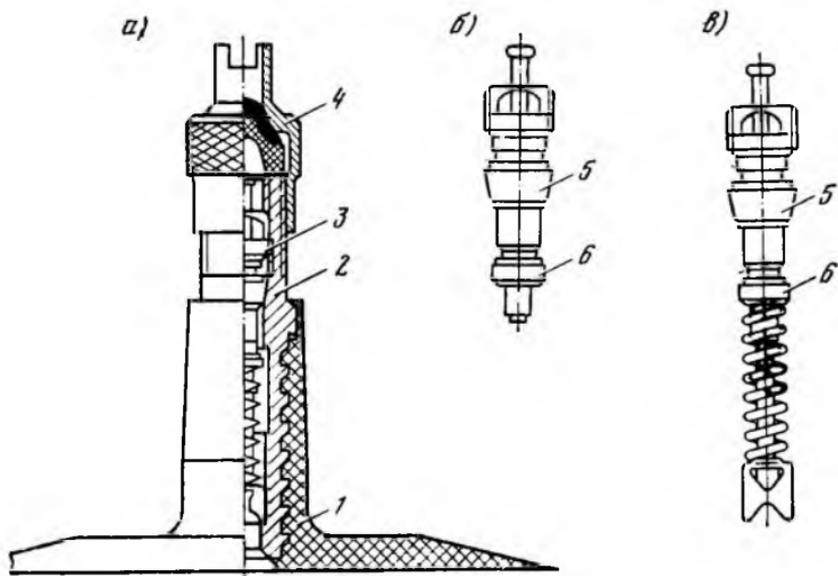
Вентиль ЛК с обрешиненным корпусом для камер легковых шин;
